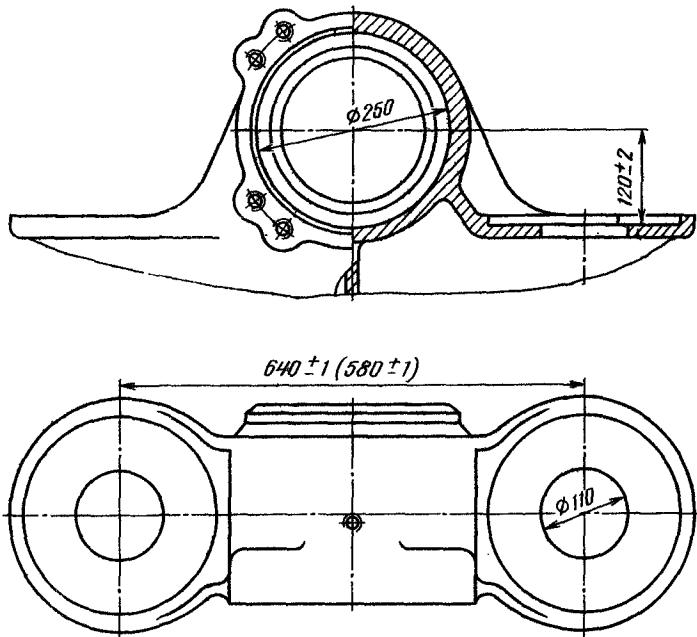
Корпуса буksы пассажирских и рефрижераторных вагонов на тележках ЦМВ (размер в скобках для тележек, изготовленных для пассажирских вагонов)
